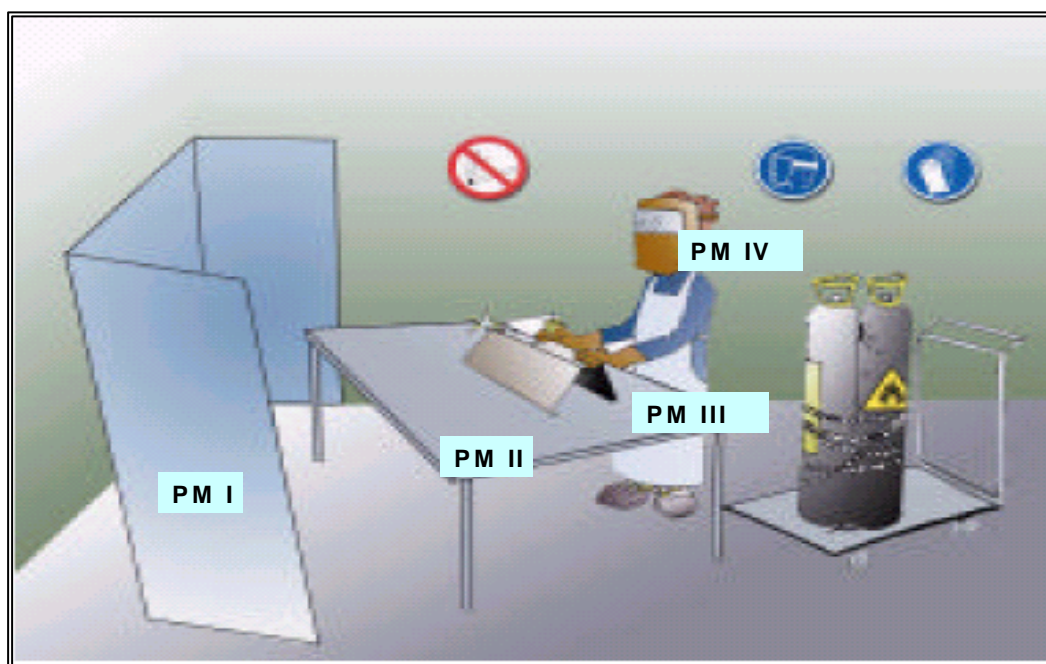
Puntos de muestreo en el taller de soldadura
